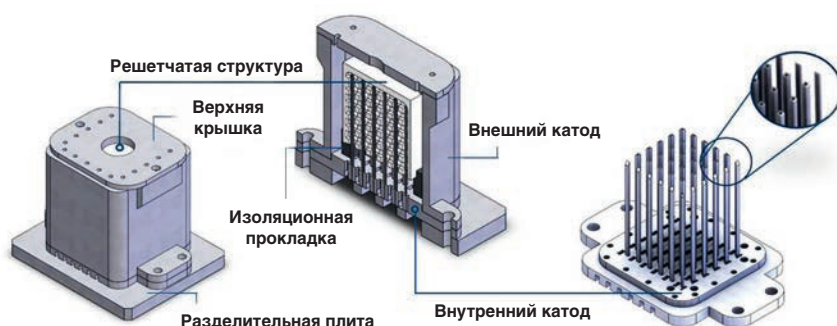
Оснастка и инструмент для дополнительной обработки решетчатой конструкции
